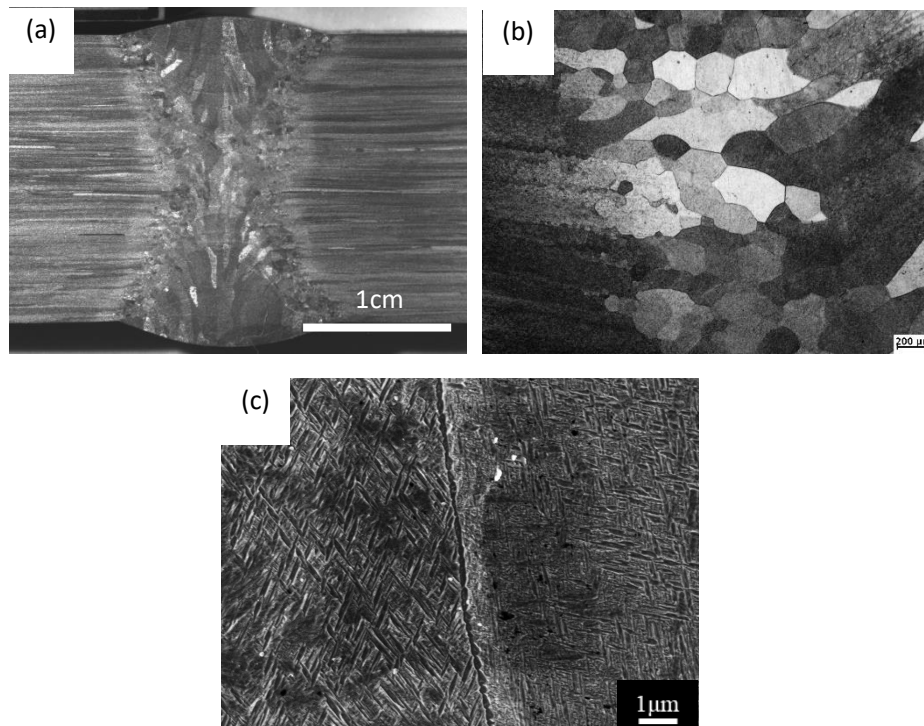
Ti5322 合金 TIG 焊接头组织
